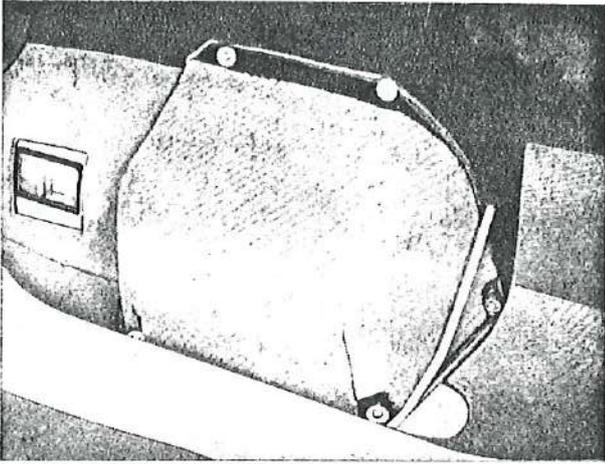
Tapa para protección del motor de arranque; es accesible por la parte interna posterior del coche.
